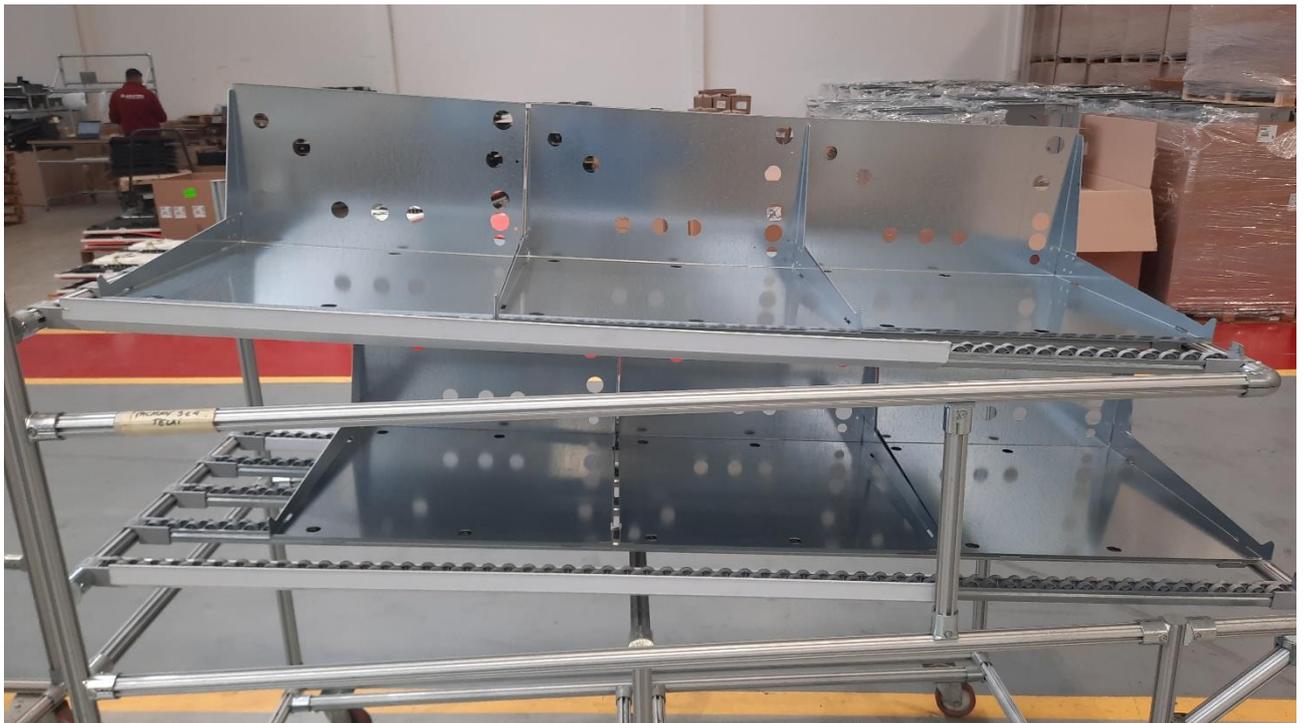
Rack per l'asservimento dei telai nella WH NEW
